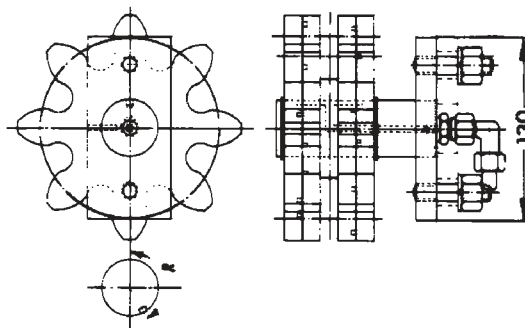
Готовое к установке устройство NV-K ZH ZV с монтажным фланцем для реверсивного вращения
